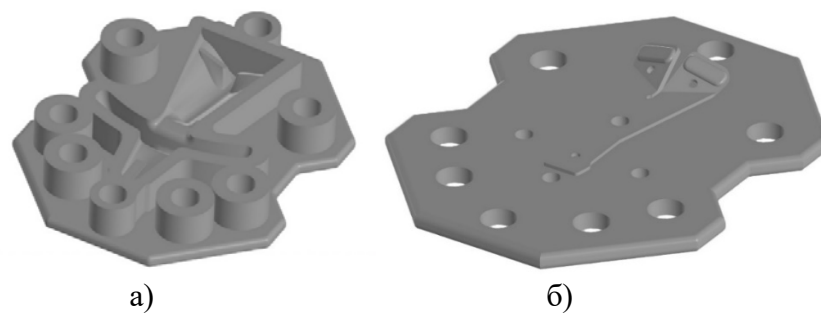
Нижняя (а) и верхняя (б) часть для отливки верхней половины аппликатора
